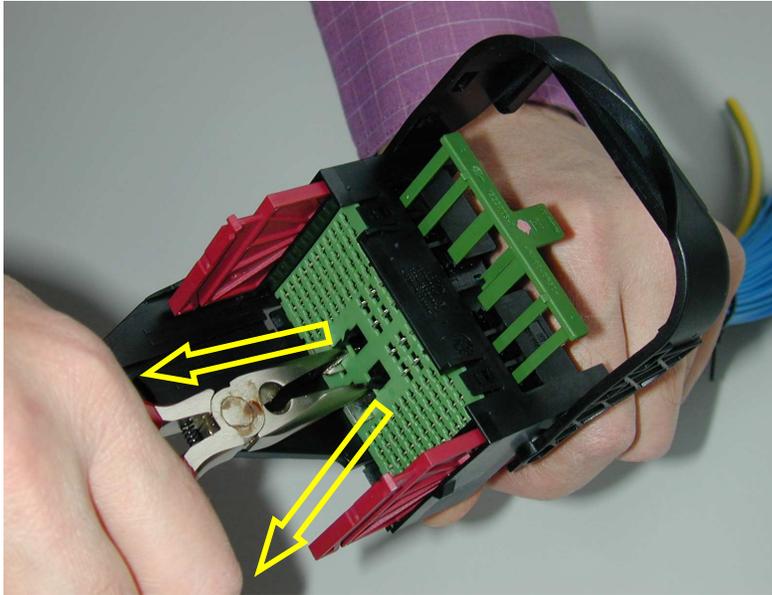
Protection Plate wie abgebildet mittels geeignetem Werkzeug ausbauen.
